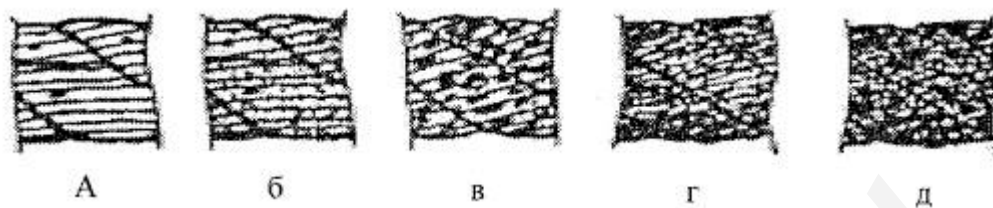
Поверхностная коррозия проволок каната крестовой свивки:
